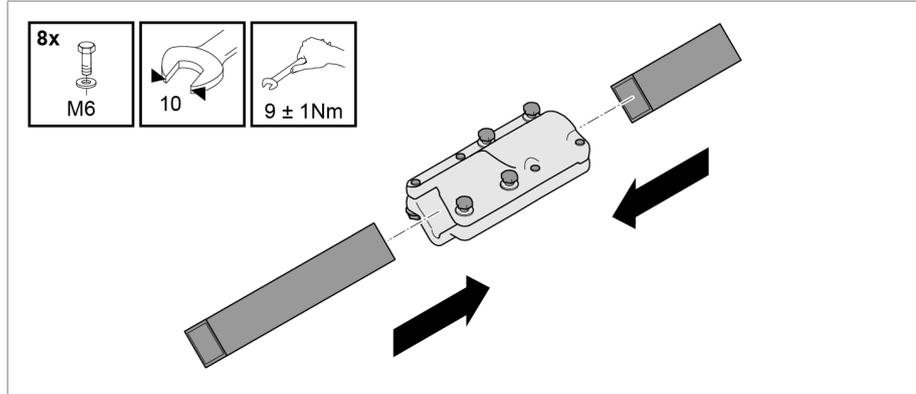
Visser le tube carré et l'isolateur à la pièce d'accouplement double
